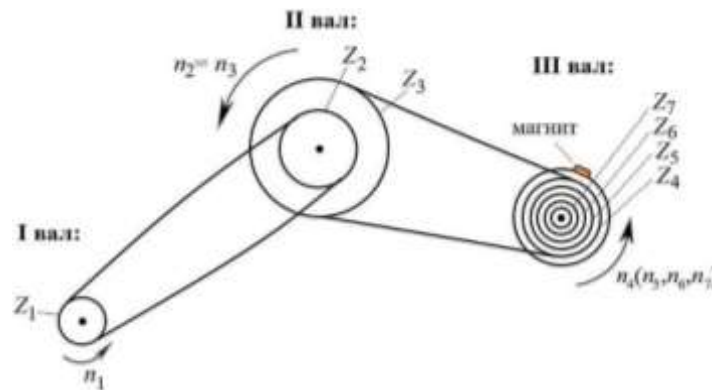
Кинематическая схема двухступенчатой цепной передачи
